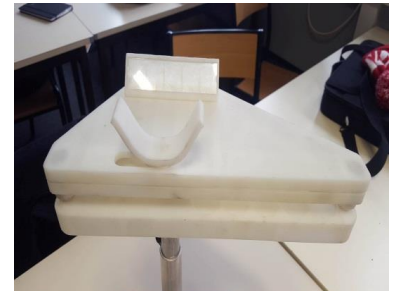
Prototypage de la mentonnière réalisée par Impression 3D
